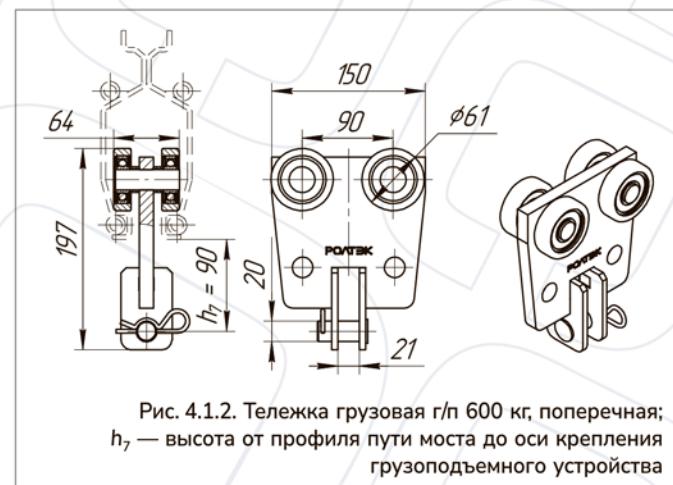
Тележка грузовая г/п 600 кг, поперечная;
